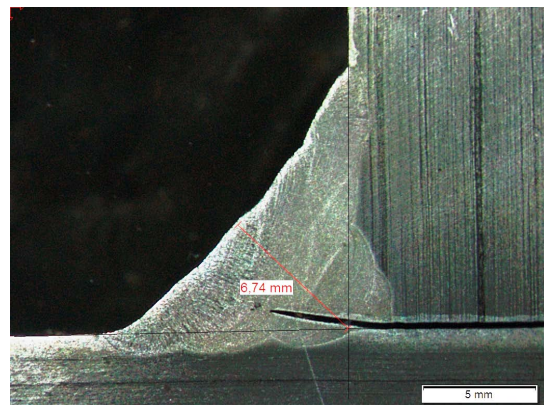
Probe G03-06, Schweißnaht FAT 36, Kreuzstoß mit Riss am Nahtansatz, niedriges Lastniveau
